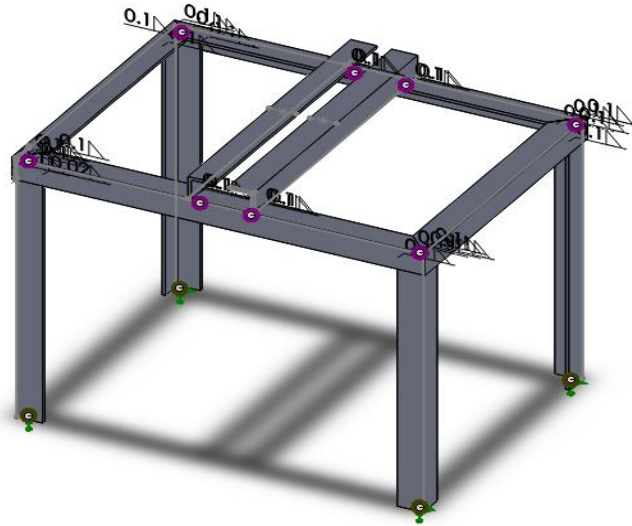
Sujeciones en las columnas de la estructura. Fuente: Jonathan Abril Investigador
